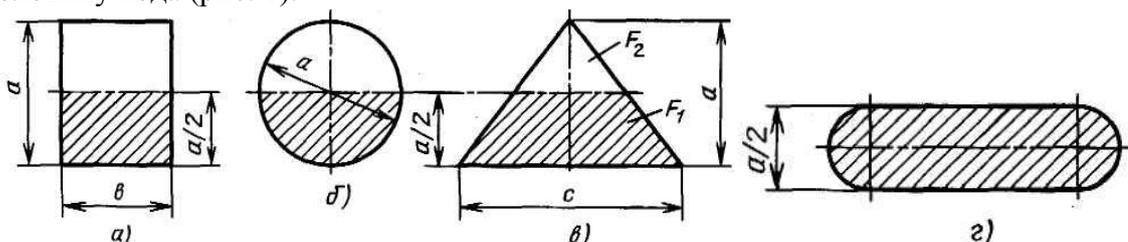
Схемы для определения степени перекрытия возможных сечений черпака:
